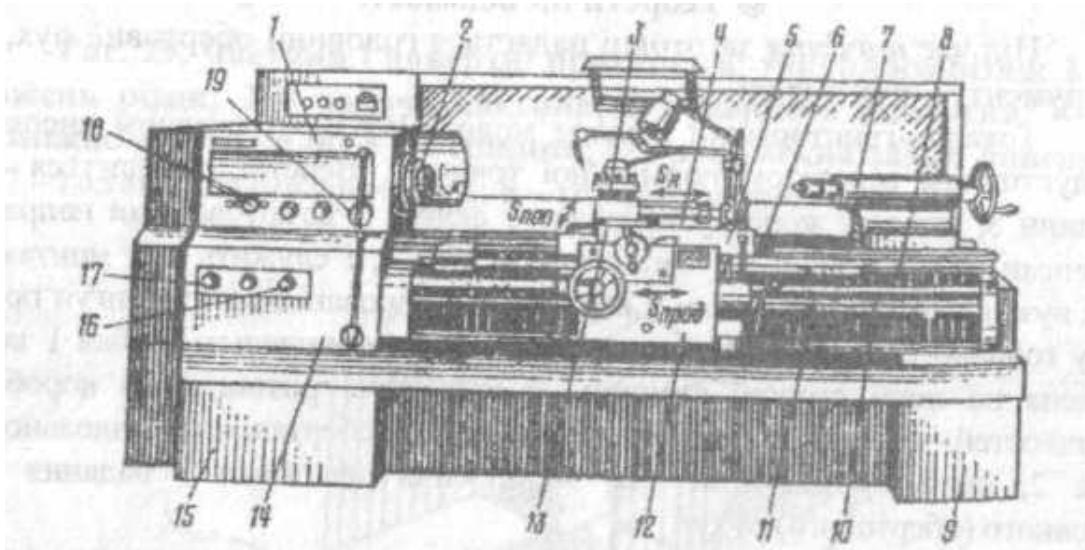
Загальний вигляд токарно-гвинторізного верстата моделі 16K20: 1 - передня бабка; 2 - шпindelний вал; 3 - супорт з різцетримачем; 4 - верхні повздовжні полози; 5 - рукоятка вмикання механічного переміщення каретки та поперечних полозок супорта; 6 - нижні повздовжні полози; 7 - задня бабка; 8 - станина; 9 - основа; 10 - ходовий гвинт; 11 - ходовий валик; 12 - фартук; 13 - поперечні полози; 14 - коробка подач; 15,16,17 - рукоятки встановлення подачі, кроку різьби, виключений механізму коробки подач; 18,19 - рукоятка встановлення частоти обертання шпинделя
